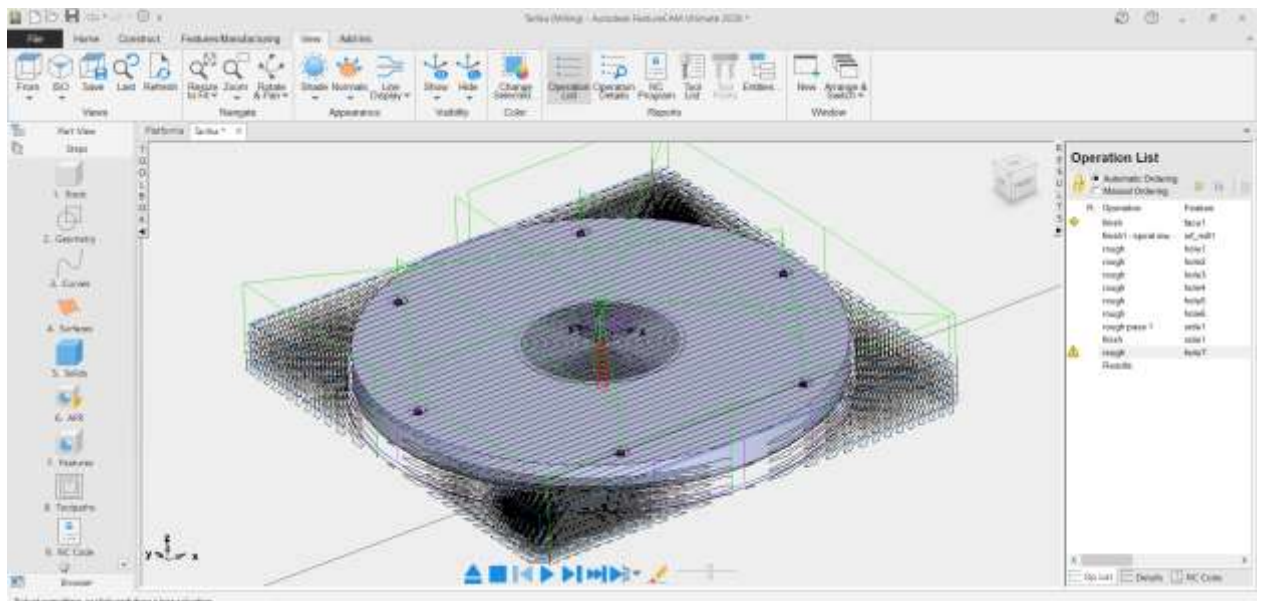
Траєкторії руху фрези для обробки деталі
